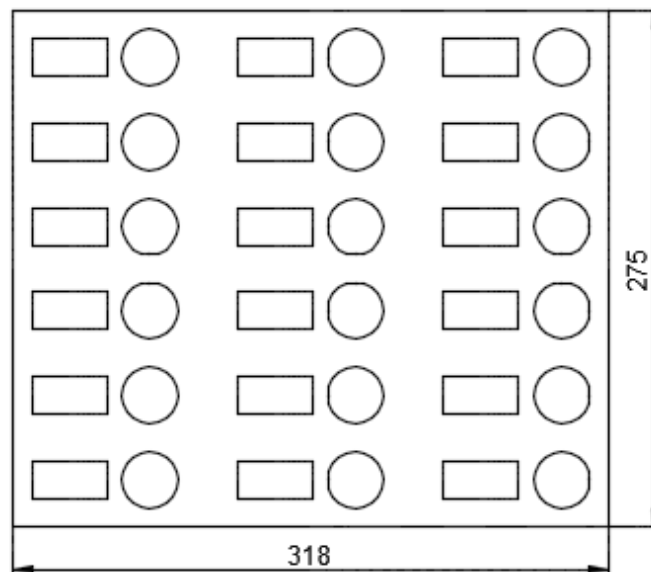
Dimensionamiento plancha base para cada compuesto. Fuente: Autor
